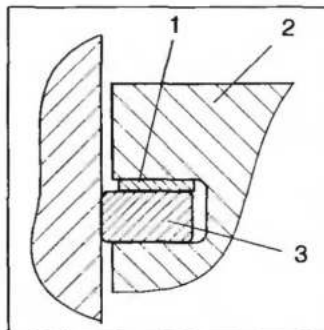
Установка дополнительного кольца при ширине канавки поршня существенно больше высоты поршневого кольца: 1 — дополнительное кольцо; 2 — поршень; 3 — основное компрессионное кольцо
